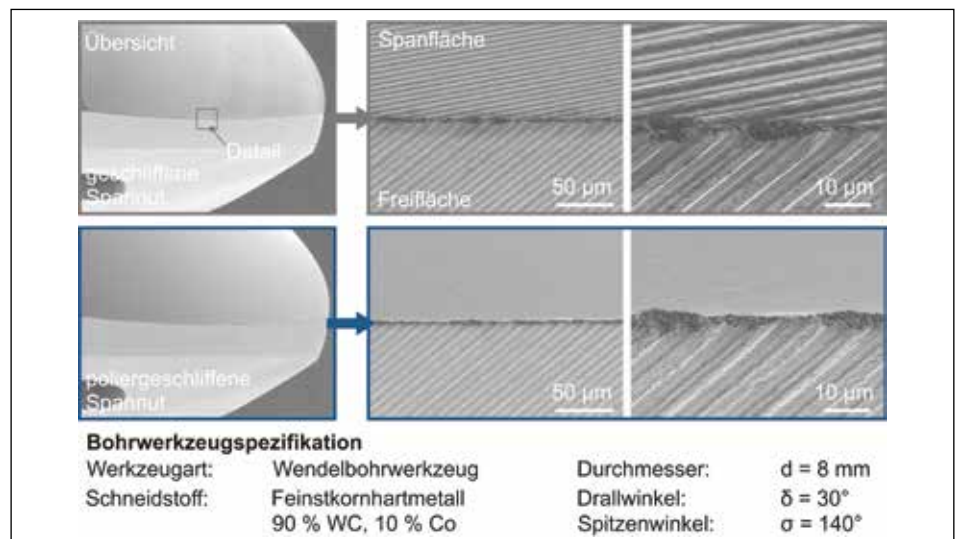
Initialzustand der Wendelbohrwerkzeuge
